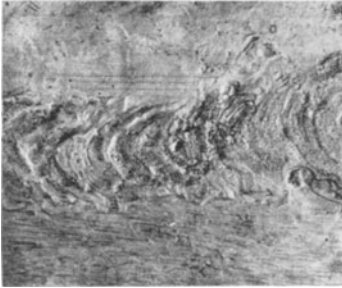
Mit dem Kohlelichtbogen geschweißtes Kupferblech.
